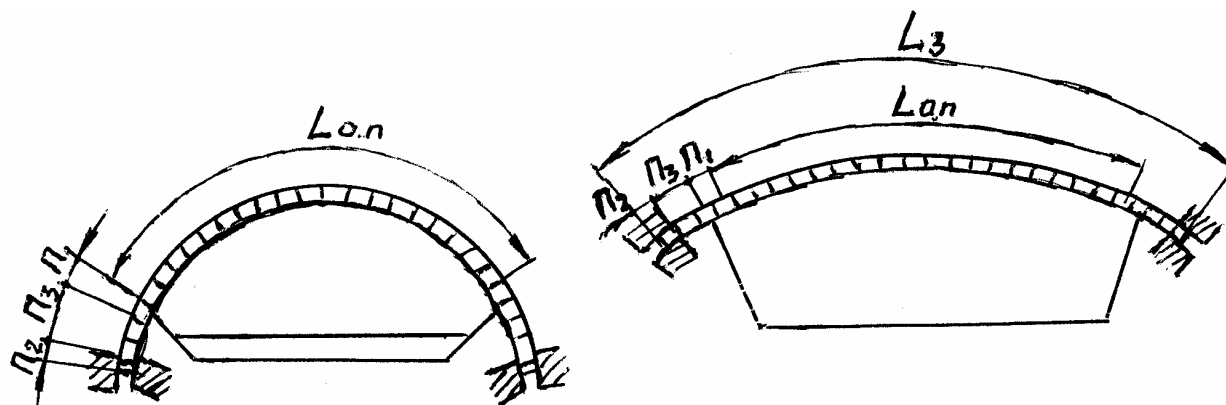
Схема определения длины заготовки обшивки двойной кривизны при обтяжке
